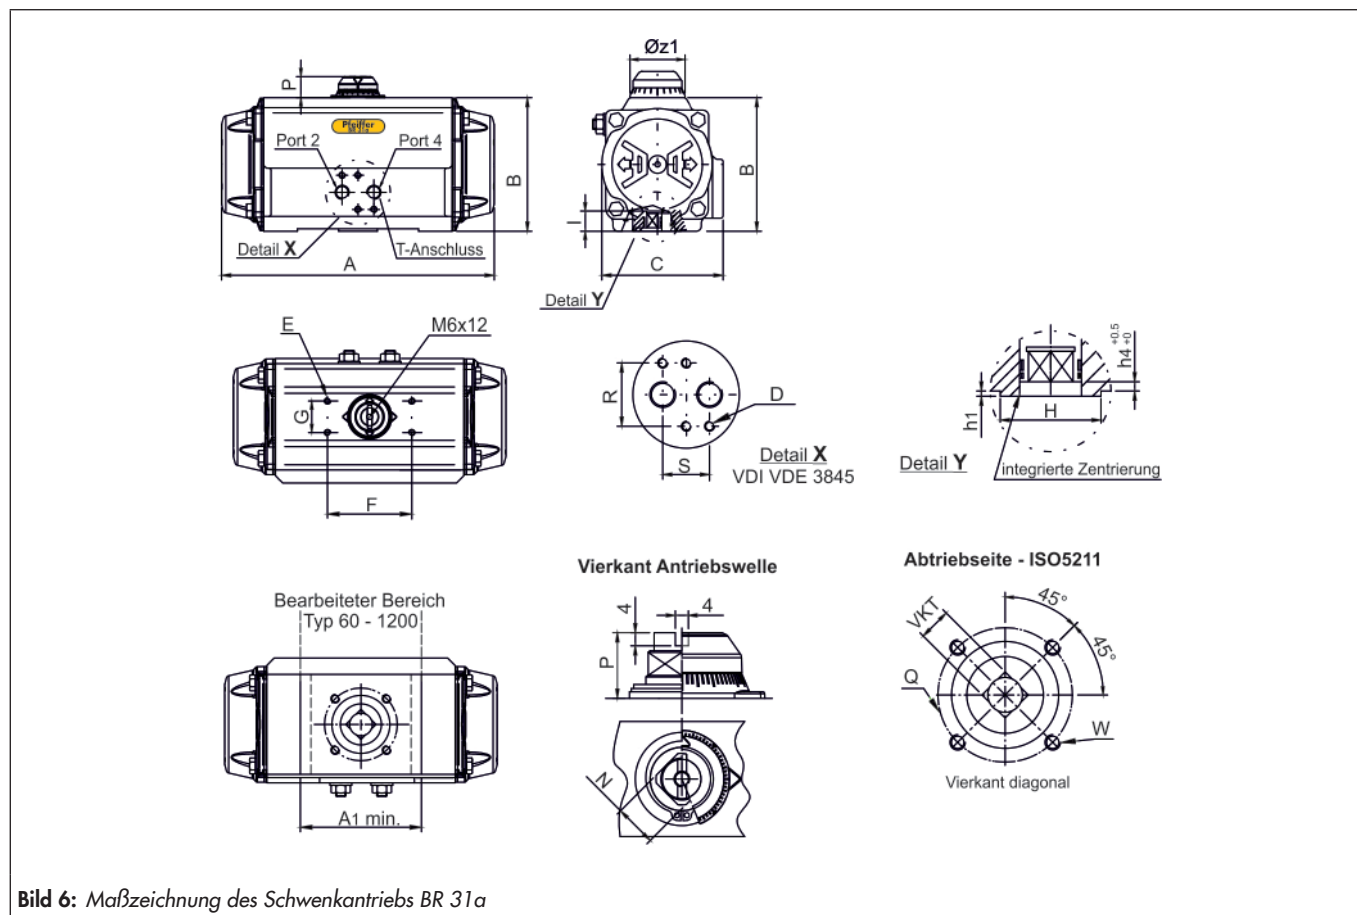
Maßzeichnung des Schwenkantriebs BR 31a
